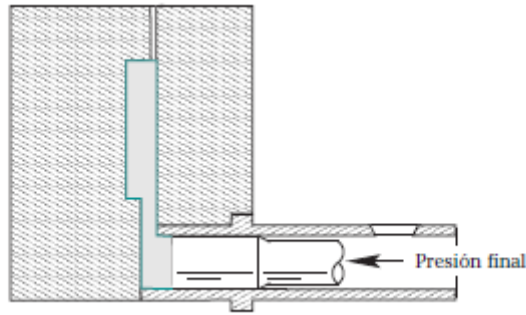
Etapa de sobrepresión del proceso de inyección en molde permanente con cámara fría horizontal.
